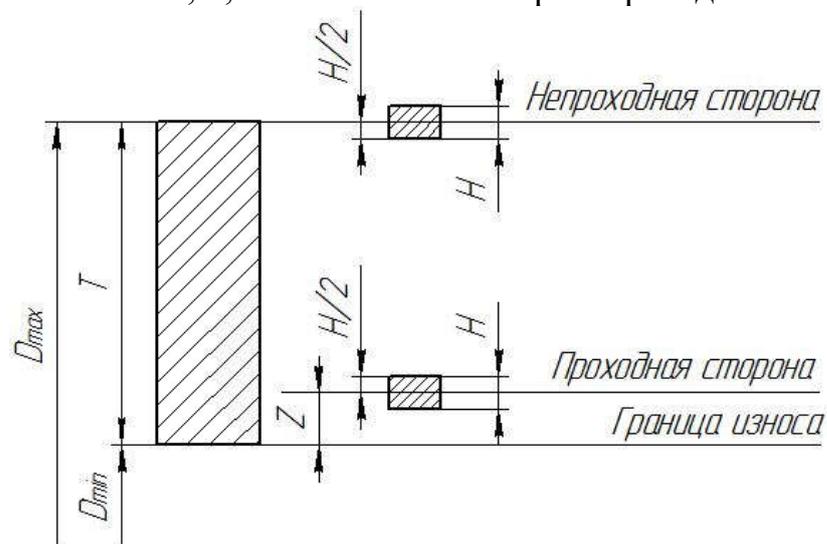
Расположение интервалов допусков для контроля отверстий квалитетов от 9 до 17 и номинальным размером до 180 мм
